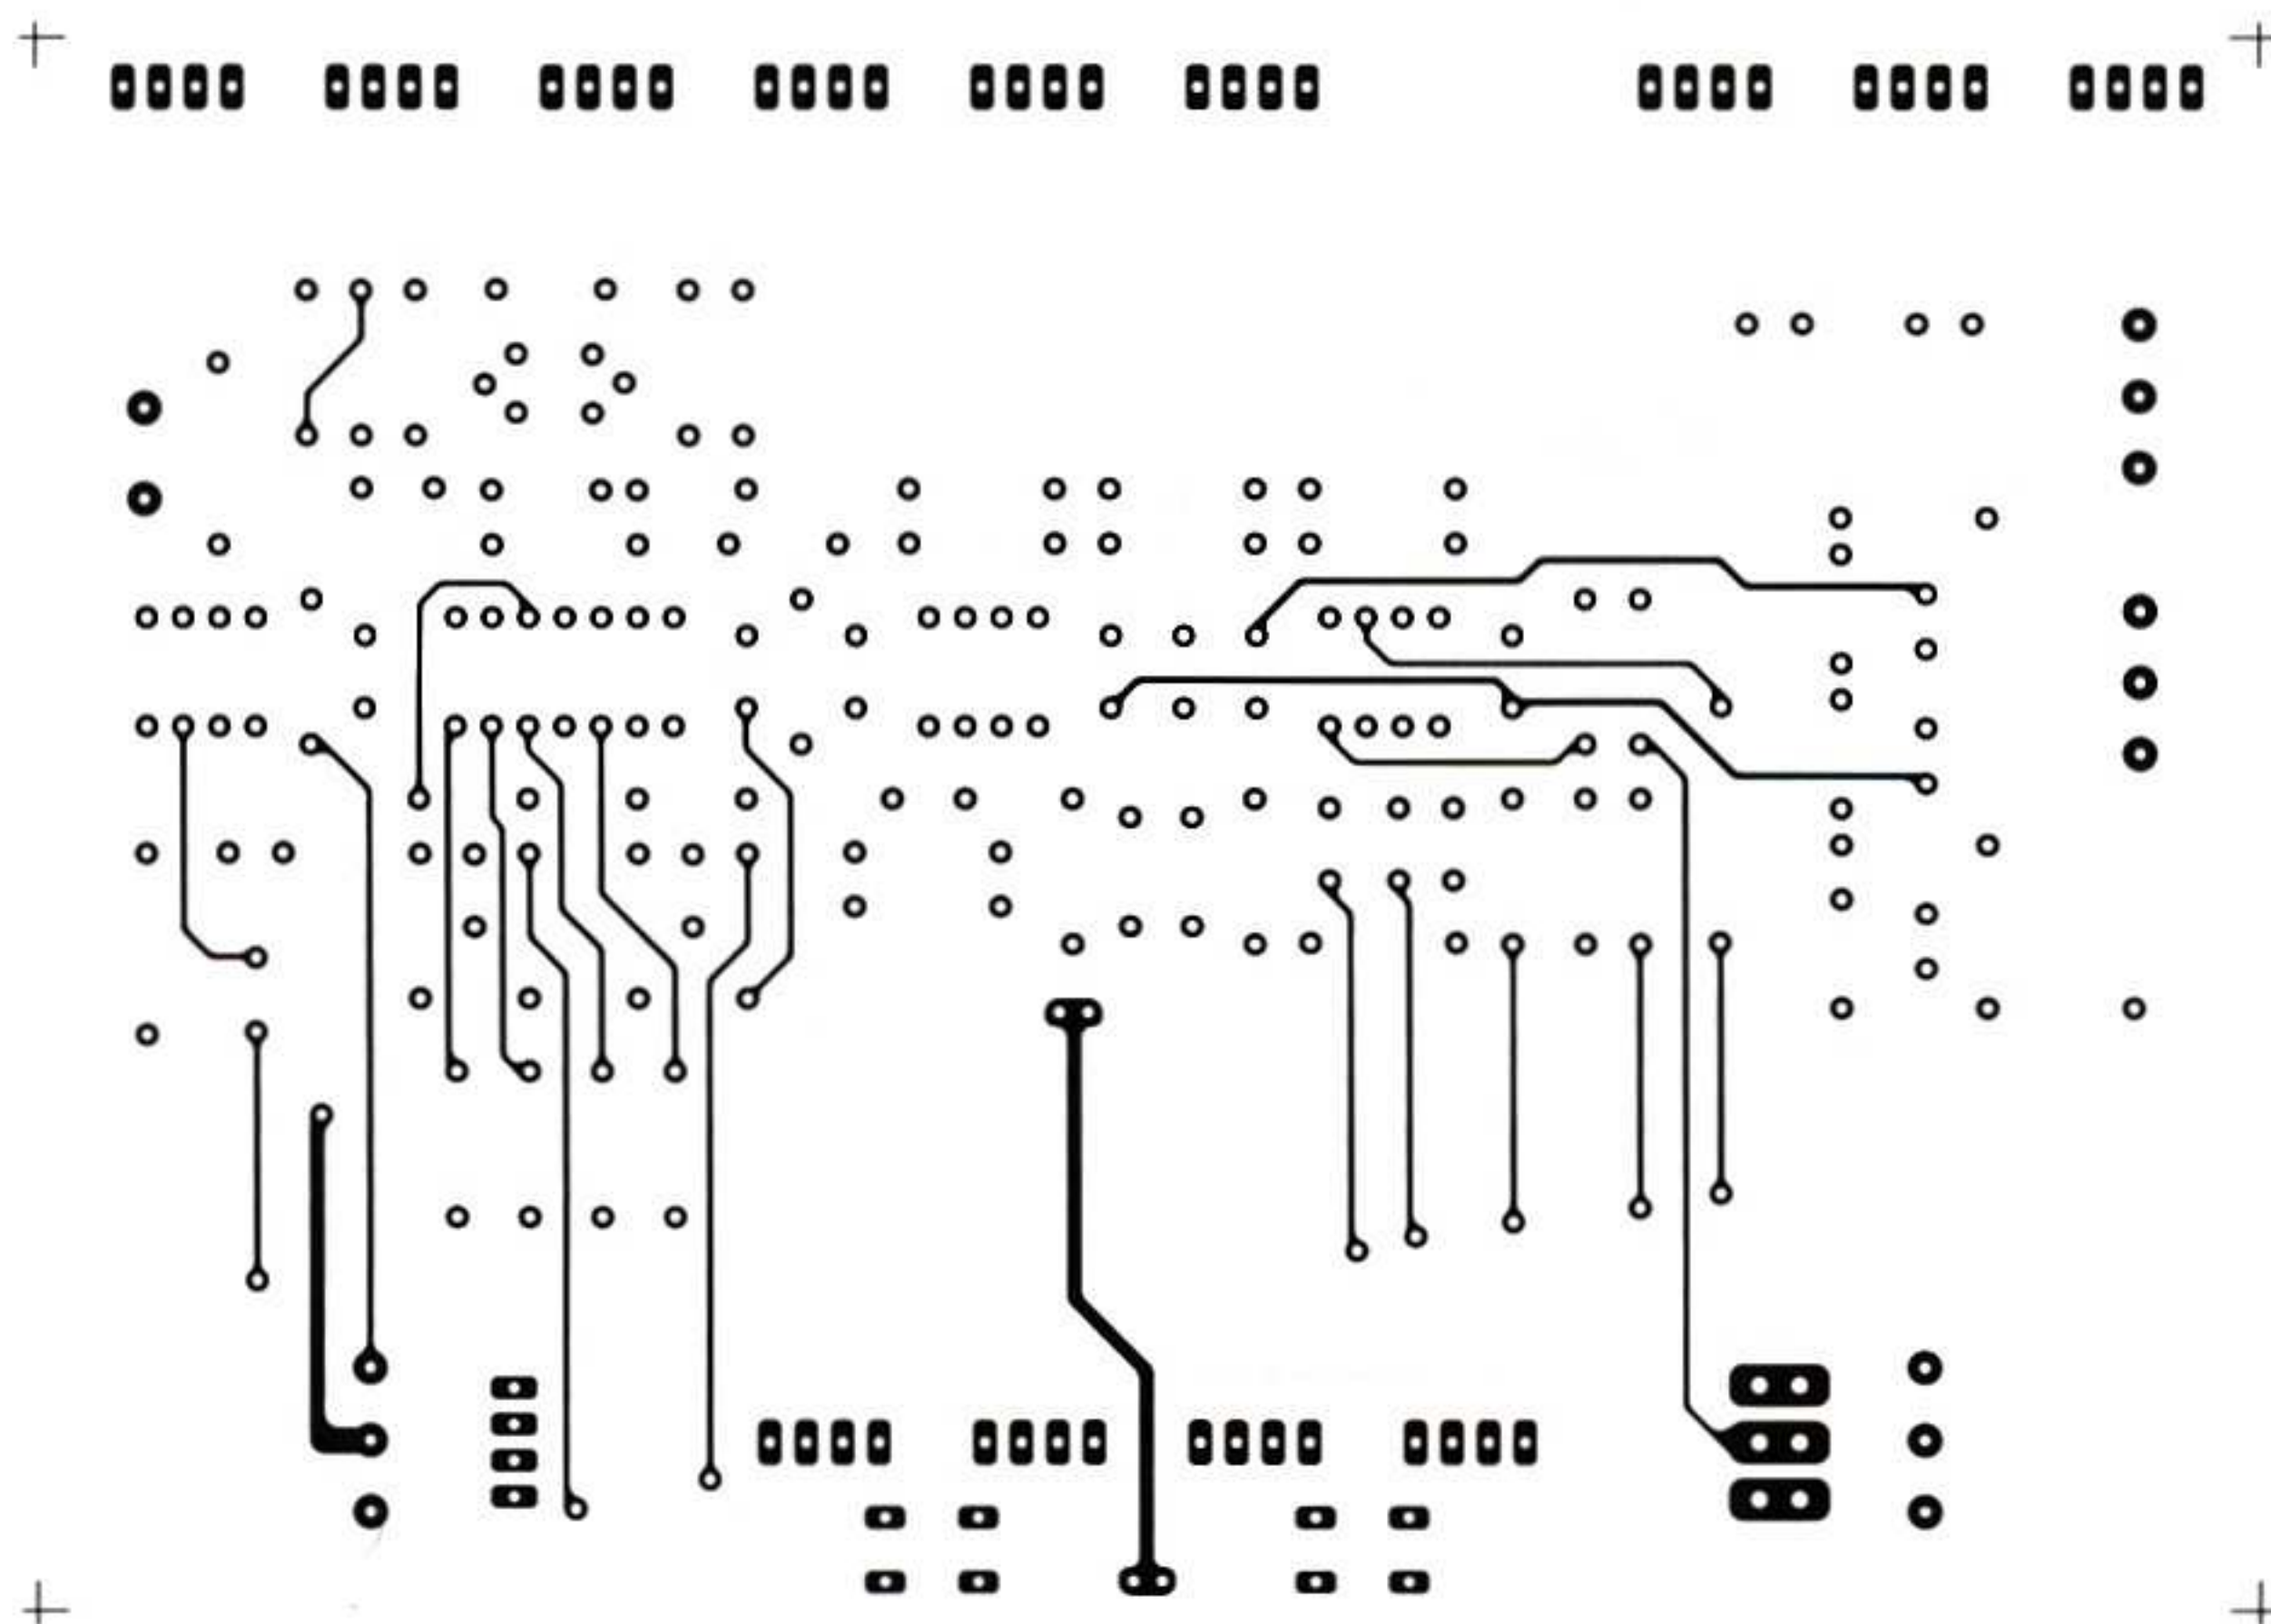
Dessin, à l'échelle 1, du circuit imprimé double face à trous métallisés de la platine de base EN3001 du MINILAB EN3000, côté soudures.
